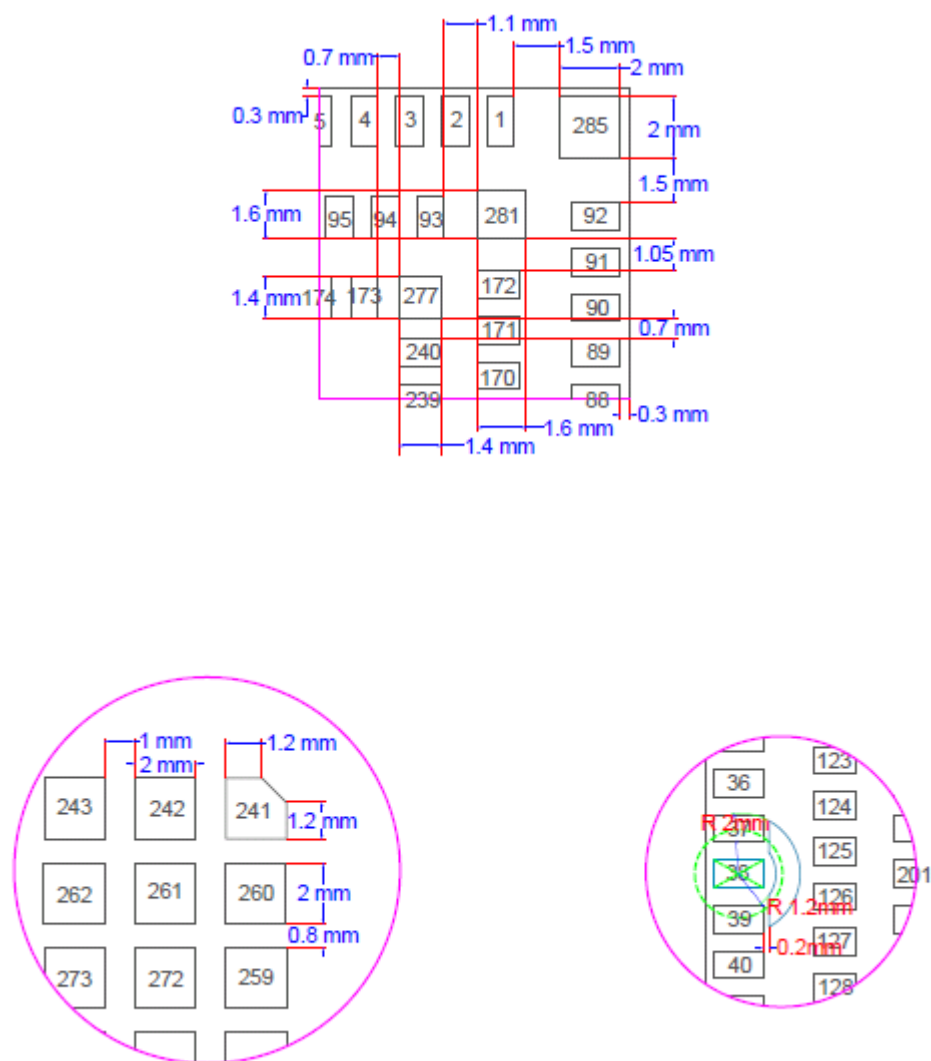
SLS4445 封装尺寸、焊盘尺寸和布局 (单位: mm) (类型 II)
